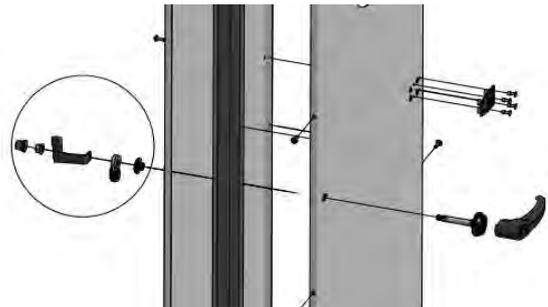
Montage du dispositif de sécurité sur le panneau de porte
